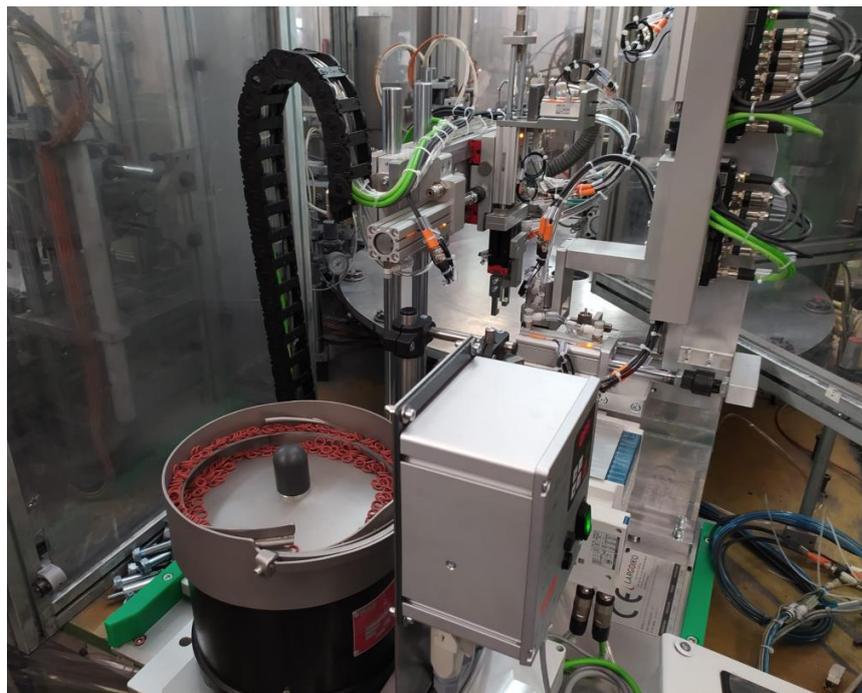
Conjunto estación instalado en cliente. Fuente:propia
